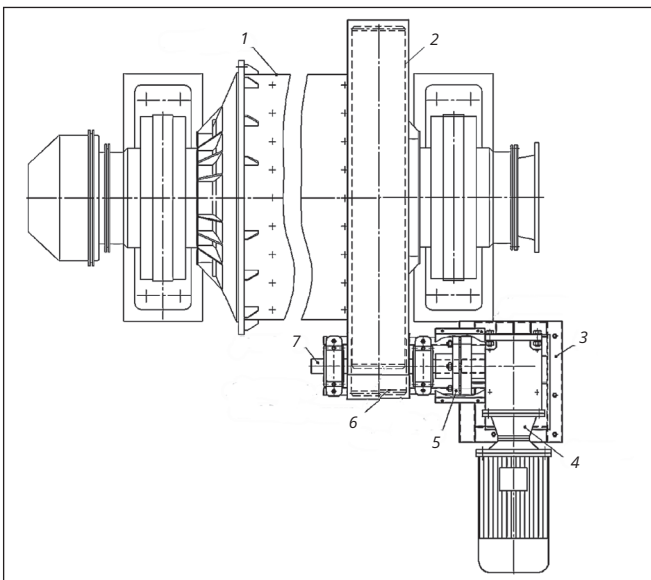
Шаровая мельница МШЦ 2,1×3,0 после модернизации: 1 – барабан; 2 – зубчатое колесо; 3 – рама; 4 – мотор-редуктор; 5 – зубчатая муфта; 6 – зубчатая шестерня; 7 – приводной вал
